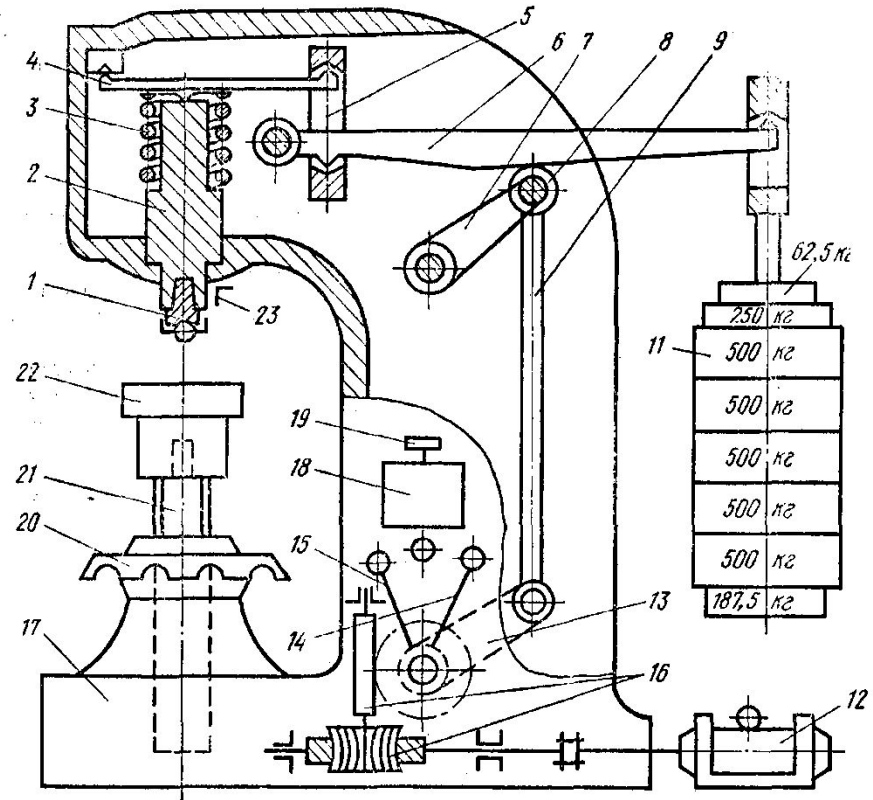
Схема устройства прибора для определения твёрдости по Бринеллю: 1 — оправка с шариком (наконечник); 2 — шпиндель; 3 — пружина; 4 — малый грузовой рычаг; 5 — серьга; 6 — большой грузовой рычаг; 7 — качающийся рычаг; 8 — опорный ролик; 9 — шток; 10 — подвеска для грузов; 11 — грузы (гири); 12 — электродвигатель; 13 — кривошип; 14 — неподвижный упор автоматического выключателя; 15 — подвижный упор автоматического выключателя; 16 — червячный редуктор; 17 — станина прибора; 18 — переключатель; 19 — пусковая кнопка; 20 — маховик с гайкой; 21 — подъёмный винт; 22 — столик для плоских образцов; 23 — неподвижный упор .
